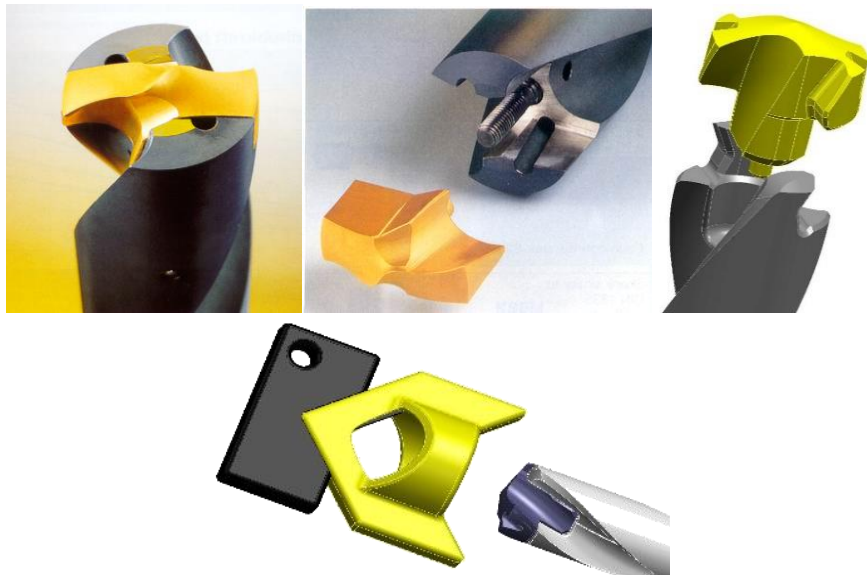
Конструкція різальної частини свердла зі змінними пластинами
